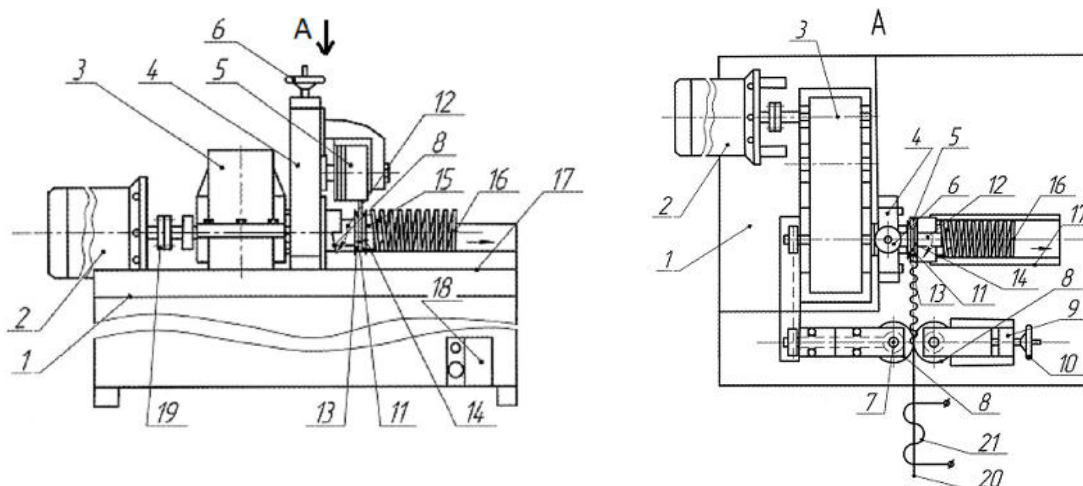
Пристрій для виготовлення гвинтових гофрованих заготовок з різним профілем гофр
